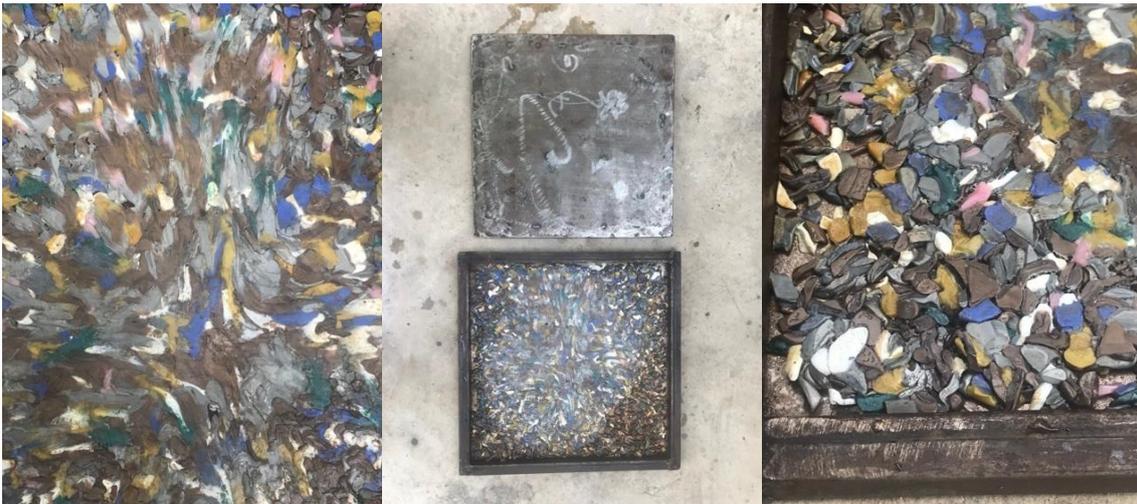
PRUEBA DE PRIMERA PLANCHA DE HDP2. FUENTE: PROPIA
